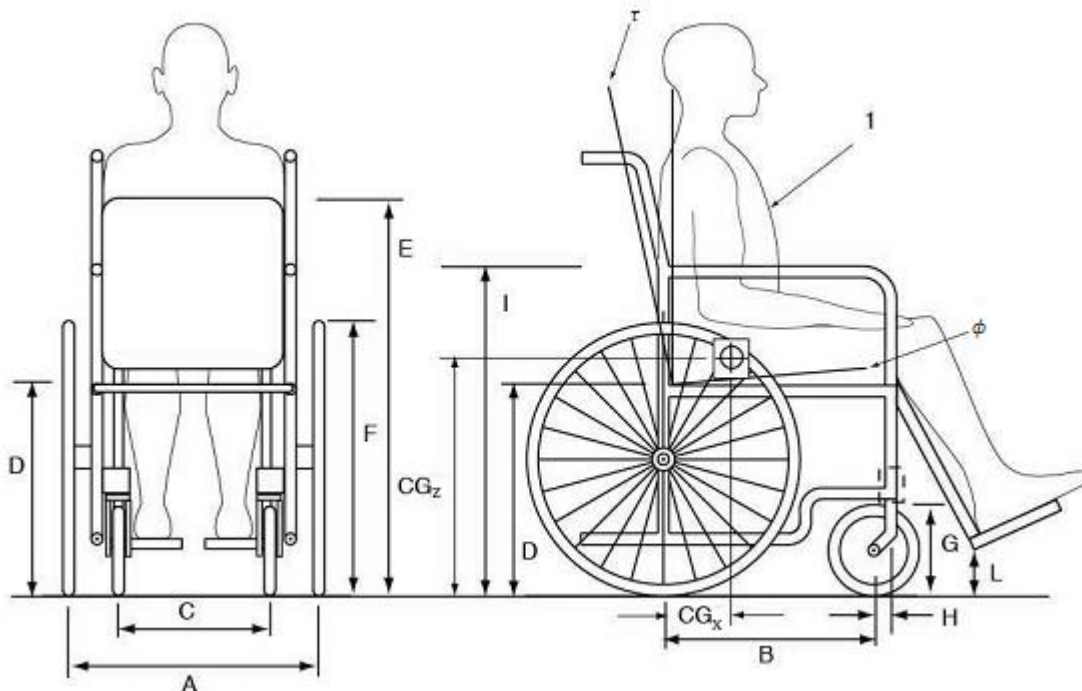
Предельные размеры имитатора кресла-коляски с ручным приводом
